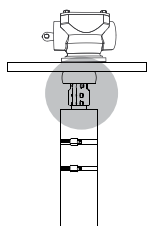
Соедините вал квадратного сечения с коническим редуктором
